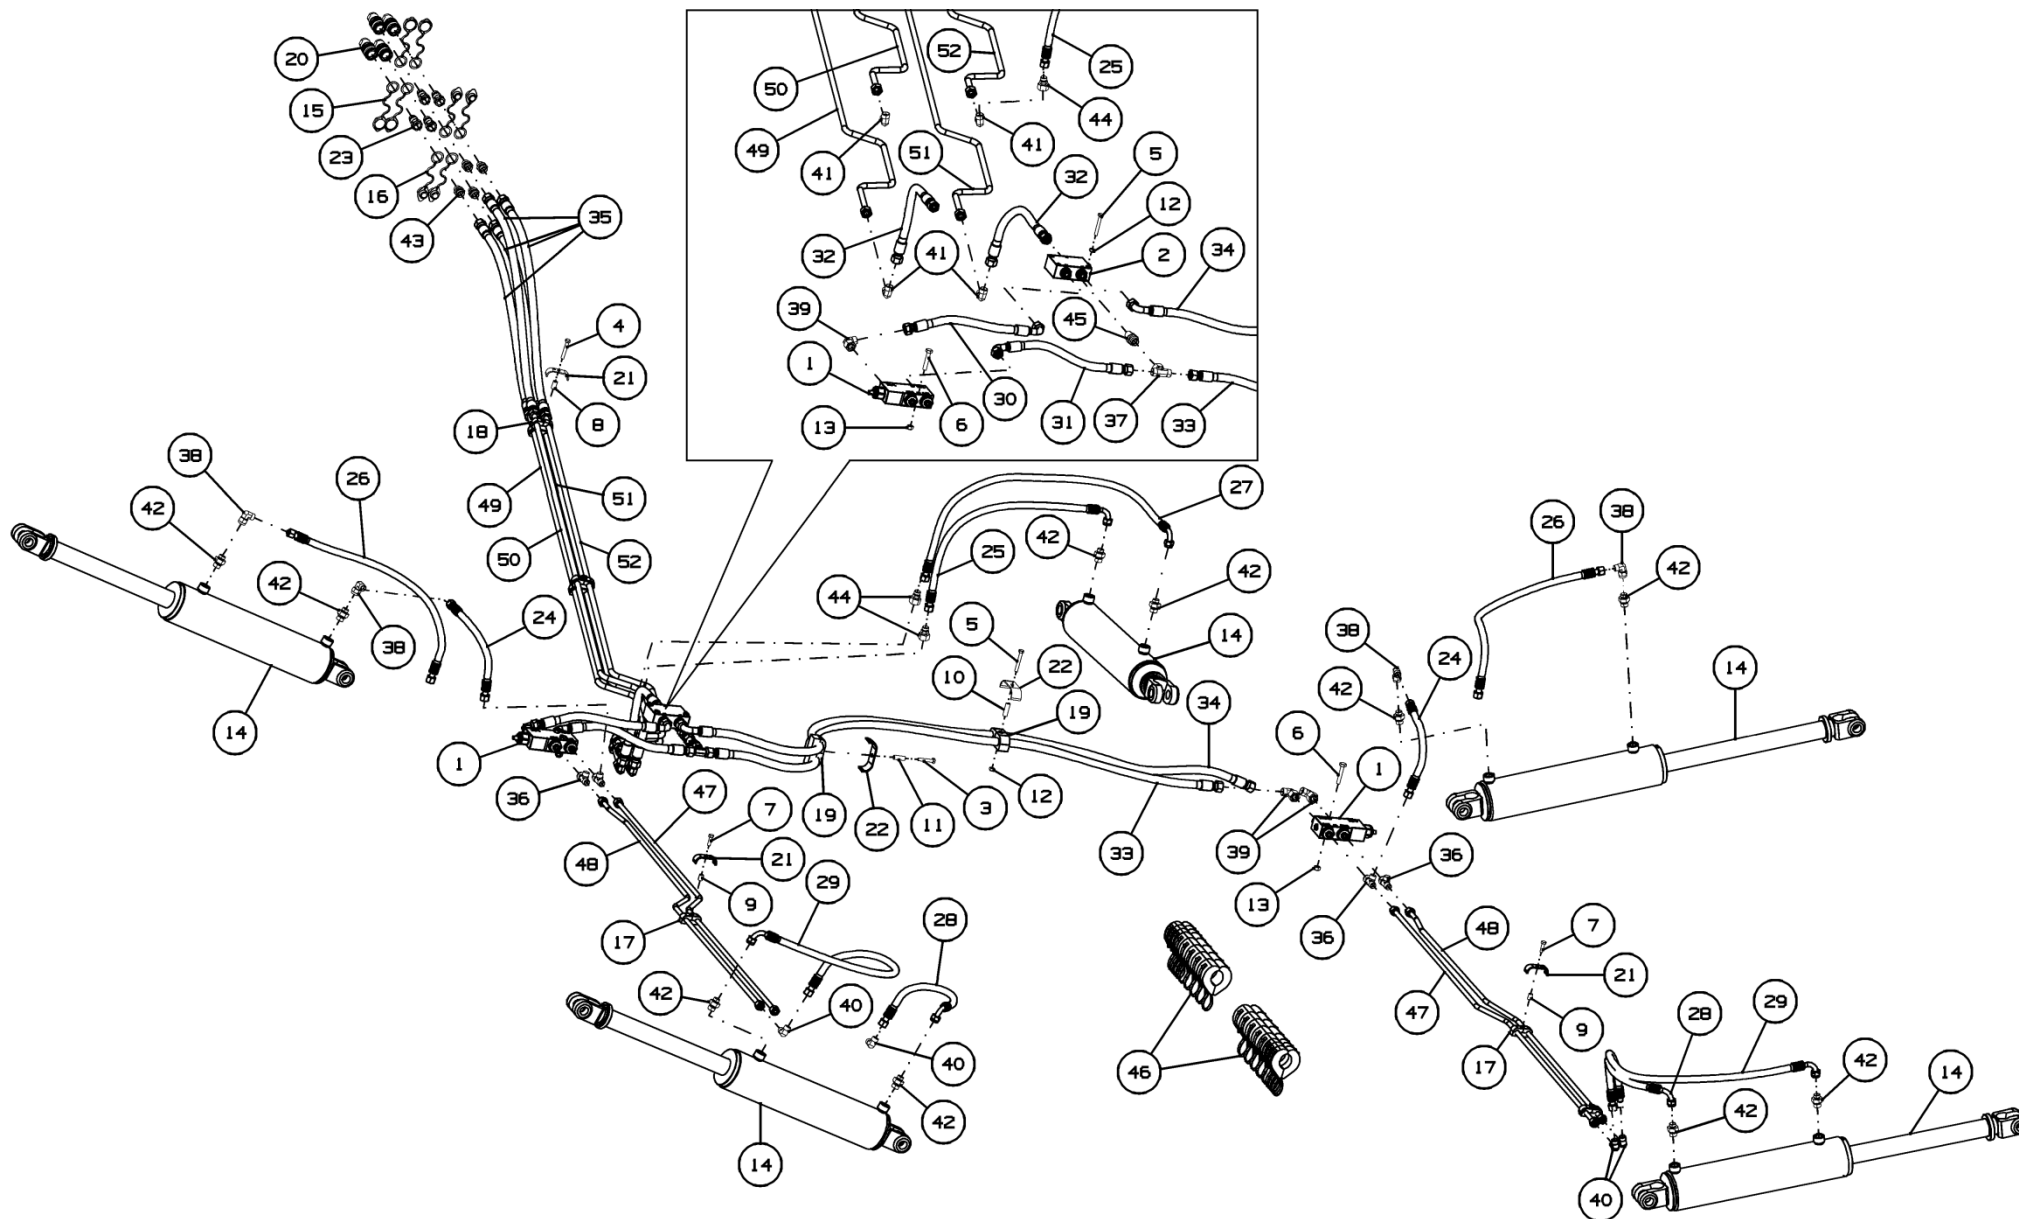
Установка гидрооборудования СГ-082.12.000А
